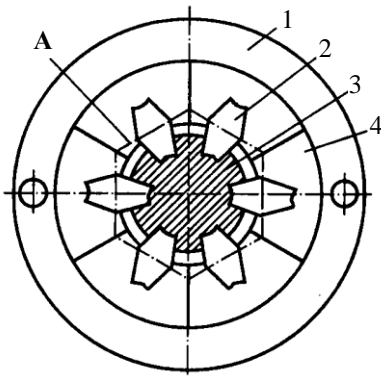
Схема накатної головки для шліценокатного верстата:
